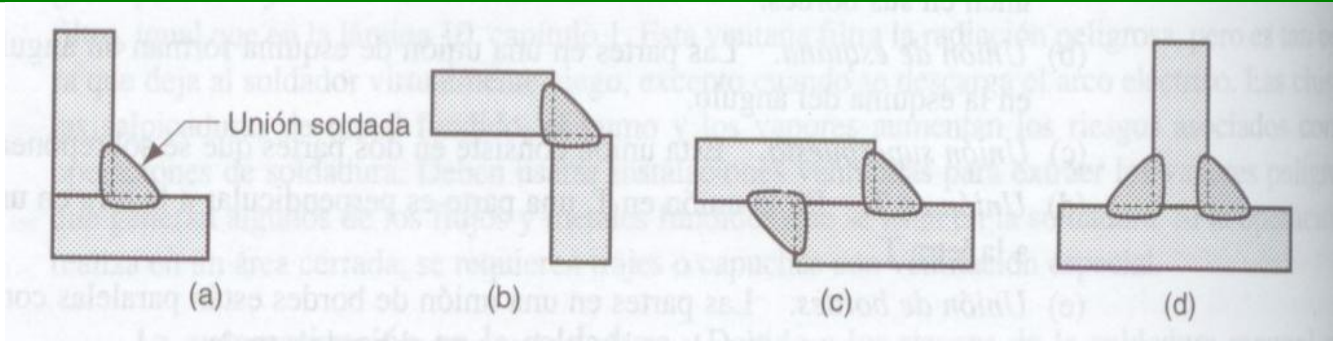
Diversas formas de soldaduras de filete: (a) unión de esquina con filete interno único; (b) unión de esquina con filete externo único; (c) unión sobrepuesta con filete doble y (d) unión en T con filete doble.
